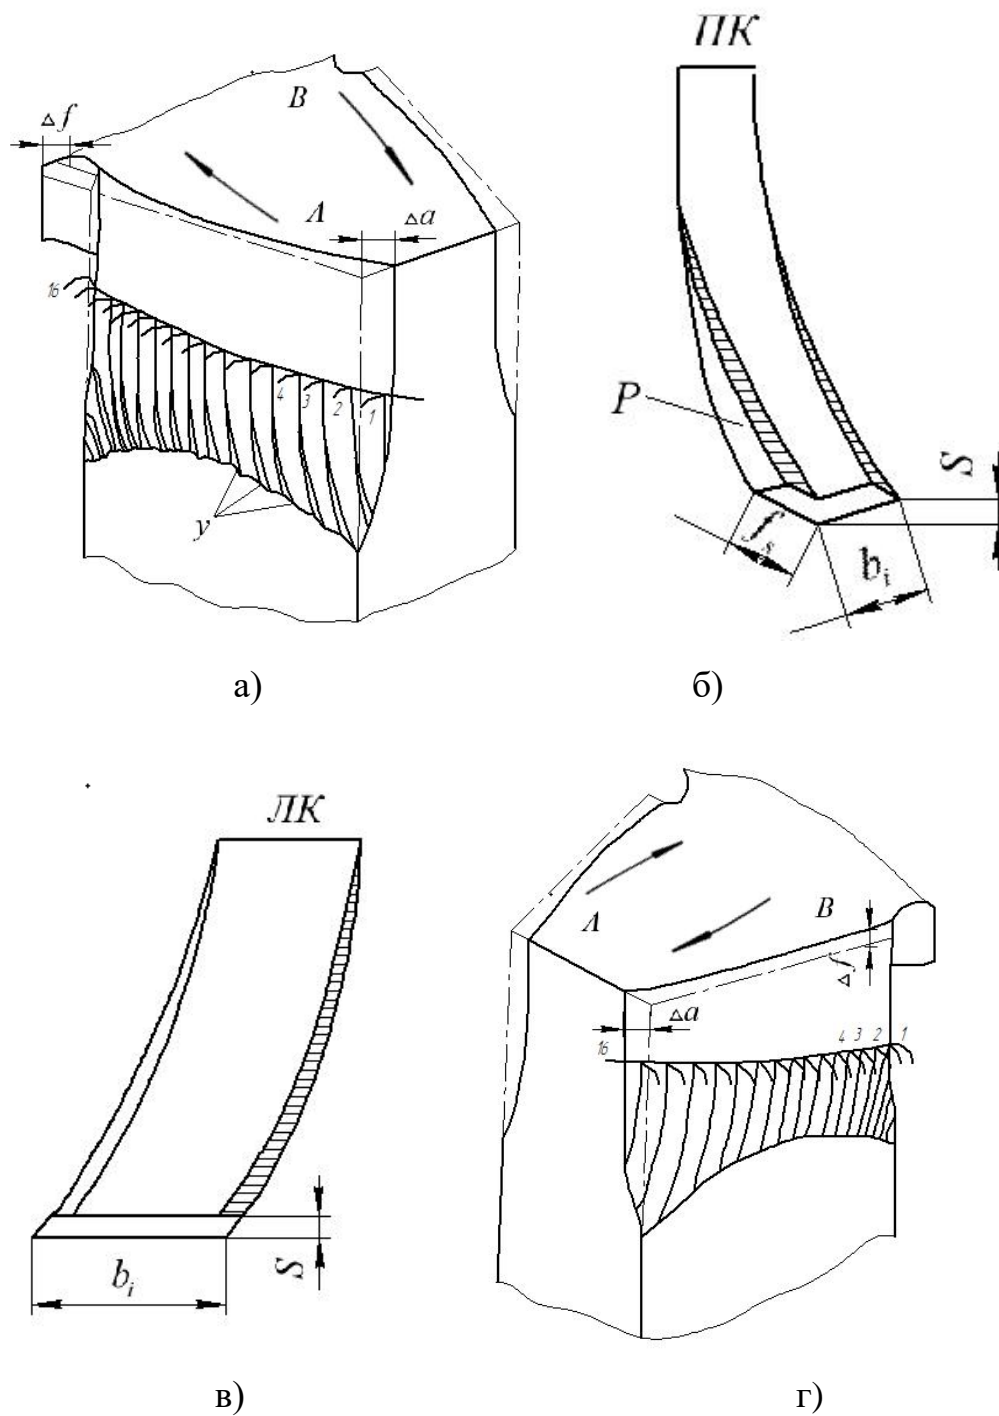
Форма шарів, зрізаних зубами правозахідної фрези з роздільною схемою формоутворення: а - утворення уступів (У) при роботі правого корпусу; б - форма шару, різаного зубами правого корпусу; в - форма шару, різаного зубами лівого корпусу; г - схема обробки поверхні зуба лівим корпусом
